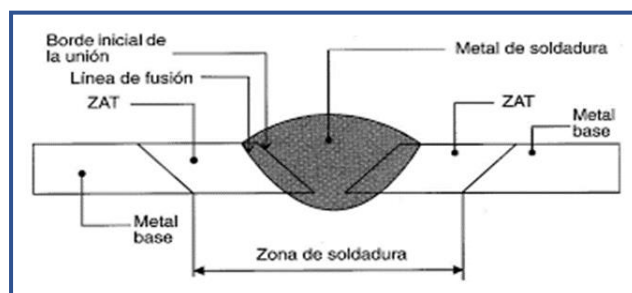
Zonas de la soldadura (Técnica Central, 2014).
